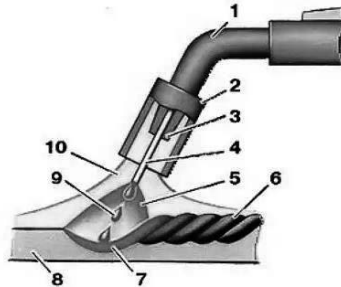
Зварювання деталі у середовищі аргону: 1 – пальник; 2 – сопло; 3 – струмопідвідний наконечник; 4 – електродний дріт; 5 – зварювальна дуга; 6 – зварний шов; 7 – зварювальна ванна; 8 – основний шов; 9 – краплі електродного металу; 10 – газовий захист
